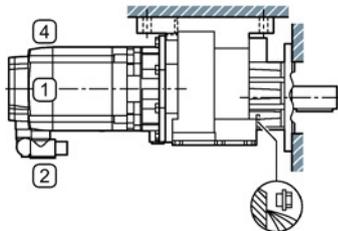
Einbaulagen für Stirnradgetriebe Z und D, Fußausführung, Baugrößen 39 - 129, 2-stufig und 3-stufig
